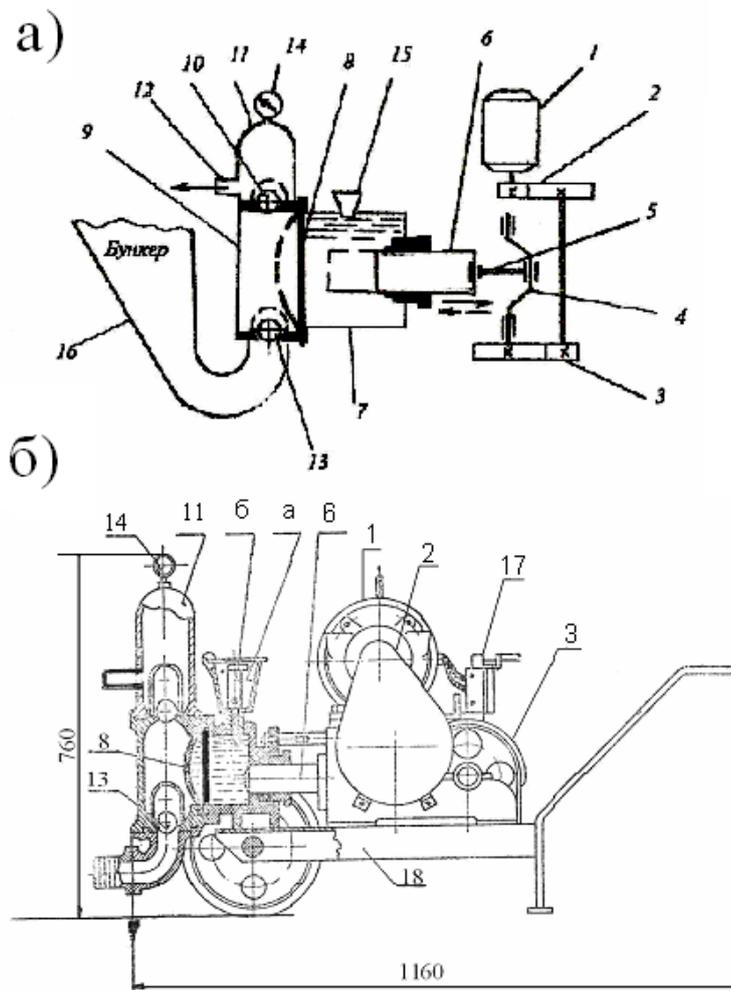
Растворонасос С-251: а) общий вид; б) конструктивная схема; 1 – электродвигатель; 2,3 – зубчатые передачи; 4 – коленчатый вал; 5 – шатун; 6 – плунжер; 7 – насосная камера; 8 – резиновая диафрагма; 9 – рабочая камера; 10 – шаровой нагнетательный клапан; 11 – воздушный колпак; 12 – нагнетательный патрубок; 13 – шаровой всасывающий клапан; 14 – манометр; 15 – заливочно - предохранительное устройство (а – воронка; б – предохранительный клапан); 16 – бункер для растворной смеси; 17 – пульт управления; 18 – ходовая тележка с колесами и рукояткой.
